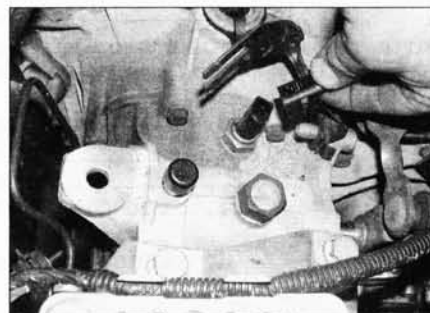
Рассоедините электрический разъем выключателя фонарей заднего хода — коробка передач O2K
